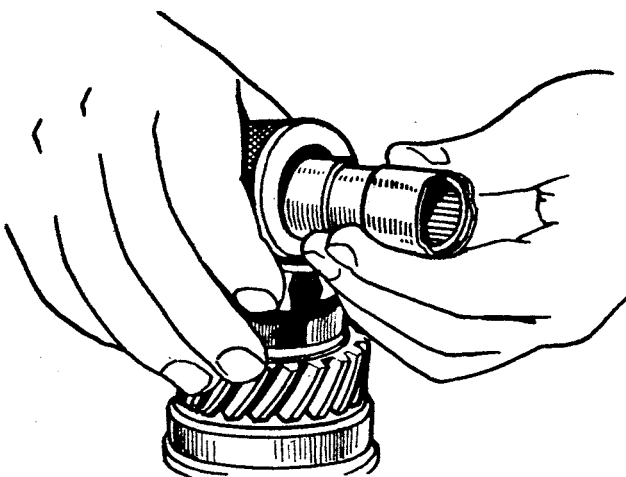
Mit einem Spezialwerkzeug werden die Nadellager auf den Antriebskolben aufgeschlagen.
